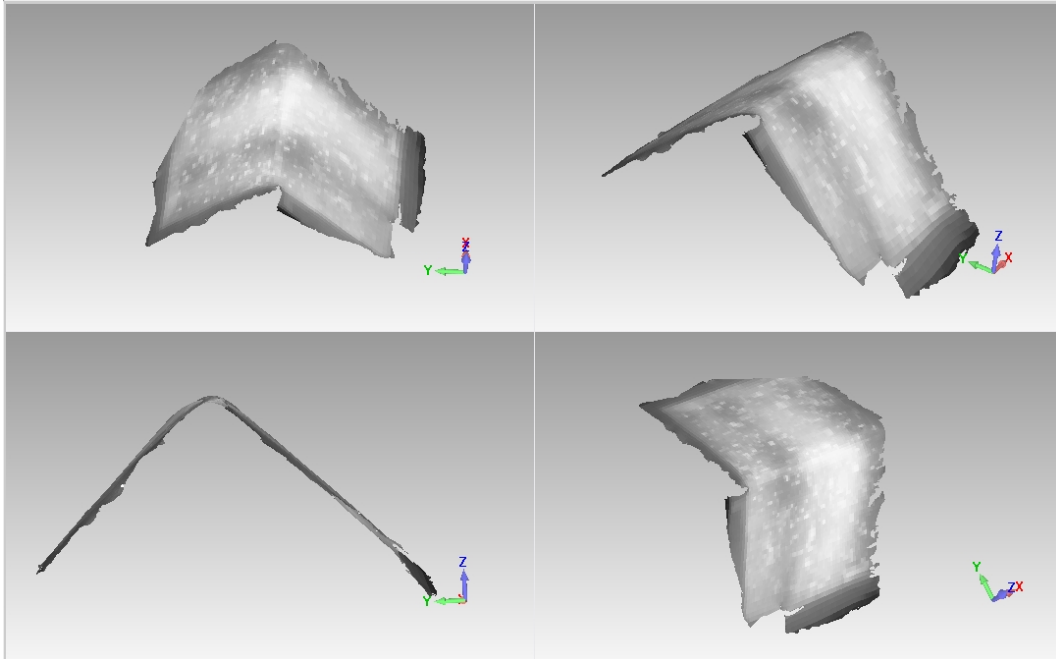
Angle droit reconstruit avec les caméras infrarouges.
